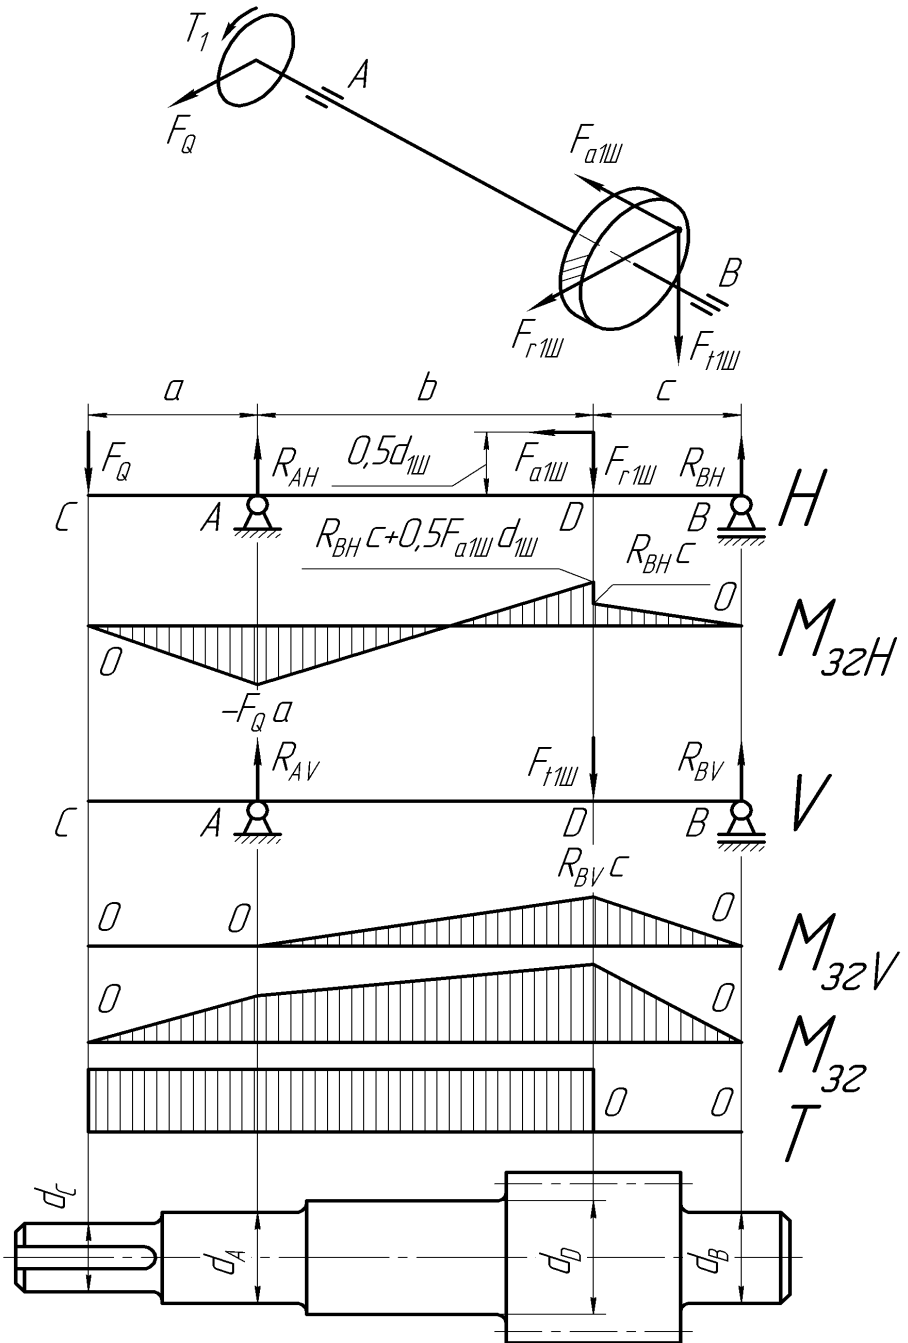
Розрахункова схема, епюри моментів і ескіз ведучого вала циліндричного двохступінчастого редуктора
